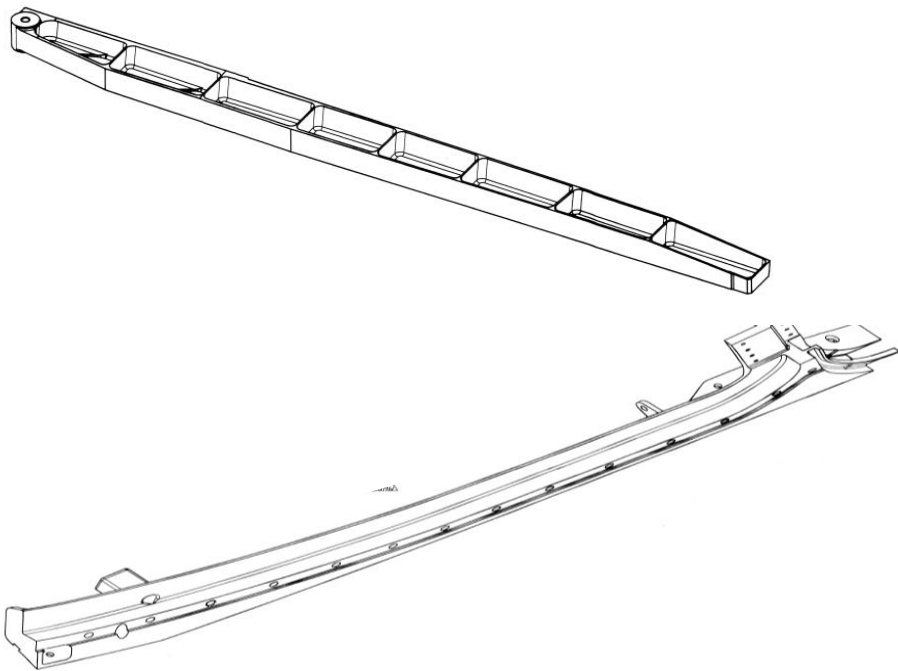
Типовые конструкции детали ”Балка”
